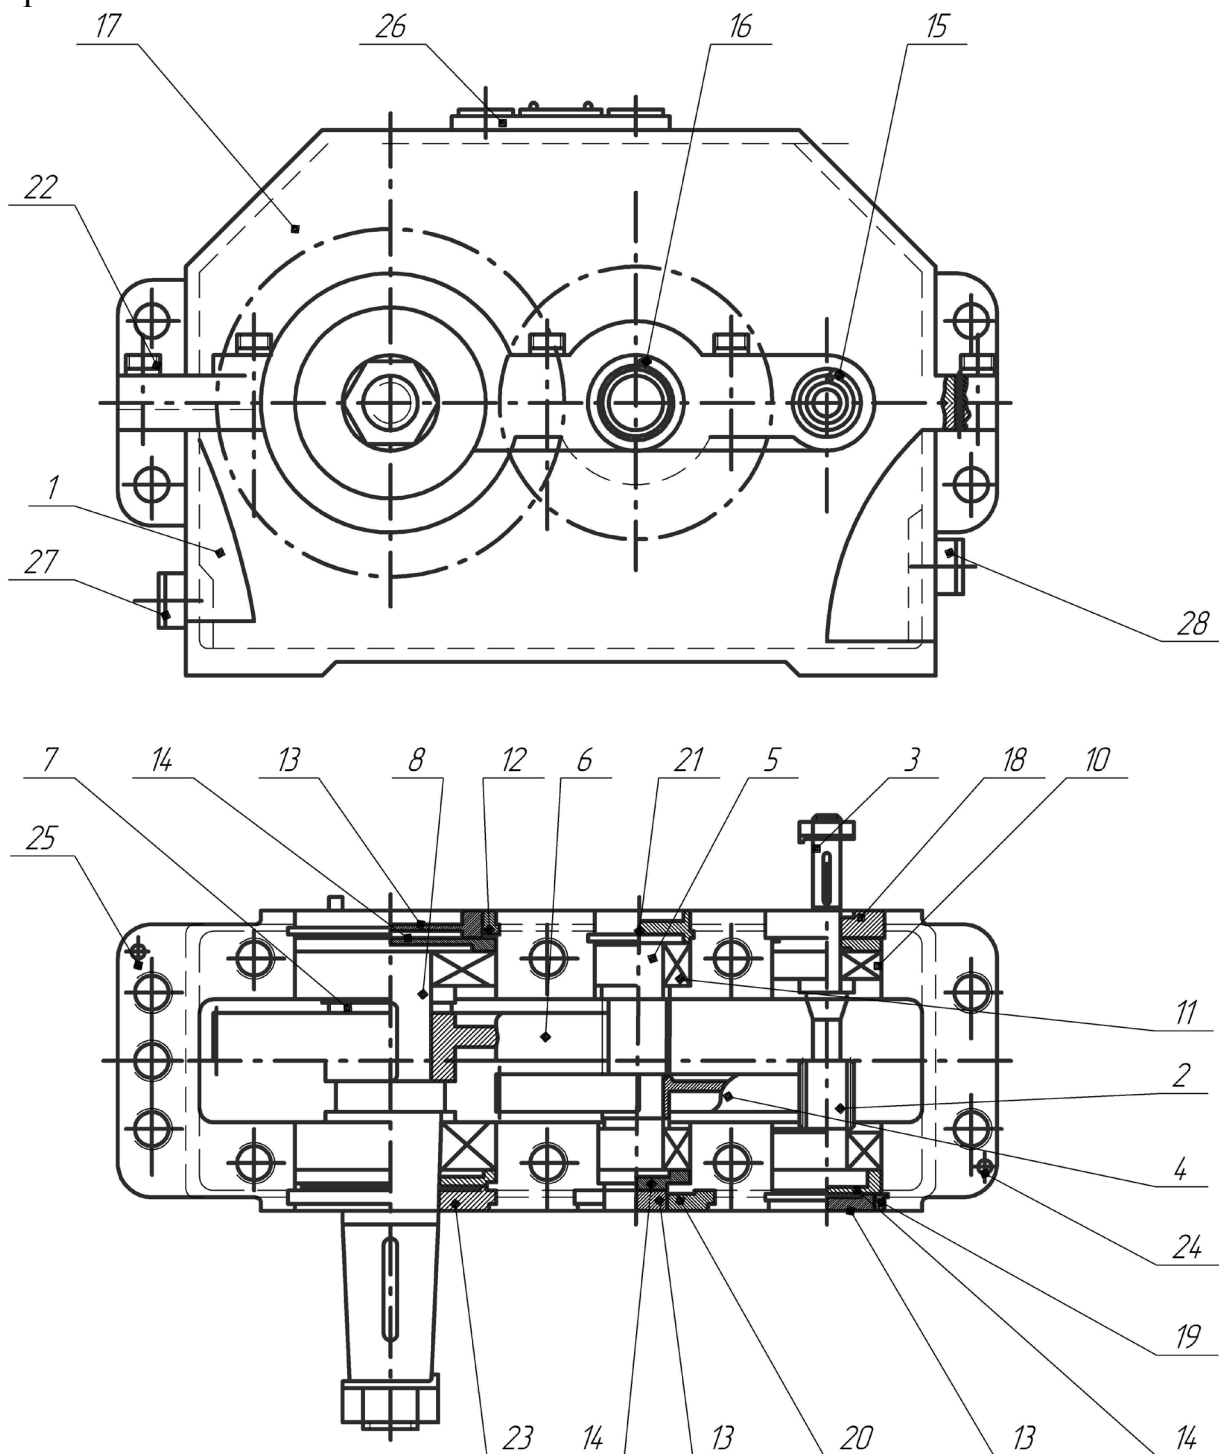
Конструкція двоступінчастого редуктора Ц2У-160
